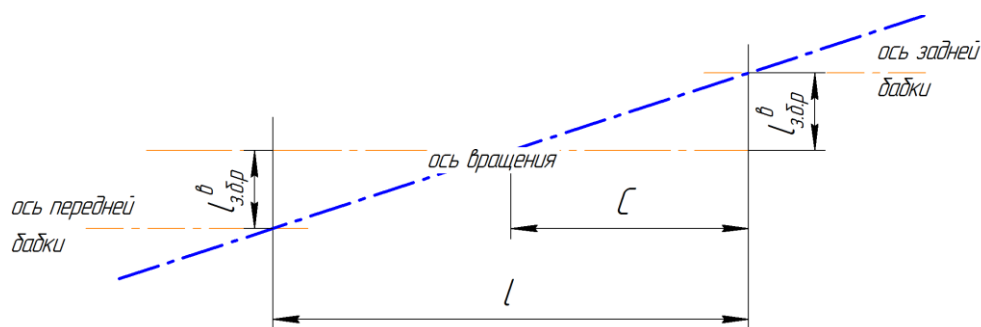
Схема установки резцов при геометрической неточности станка по вертикали
